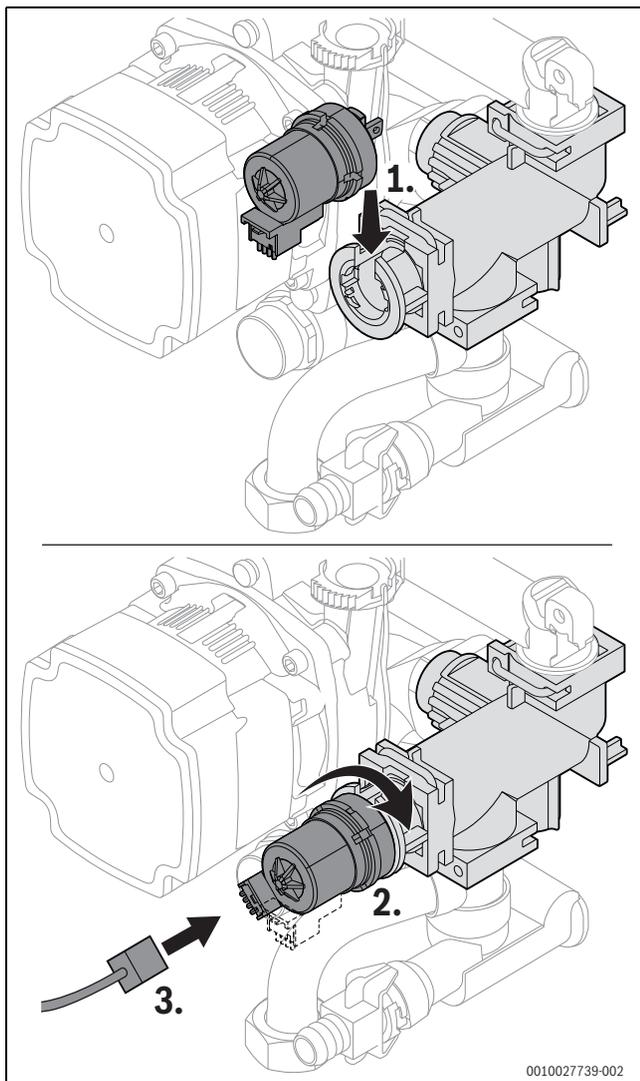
Montare il motore sulla valvola a 3 vie (variante senza viti)
